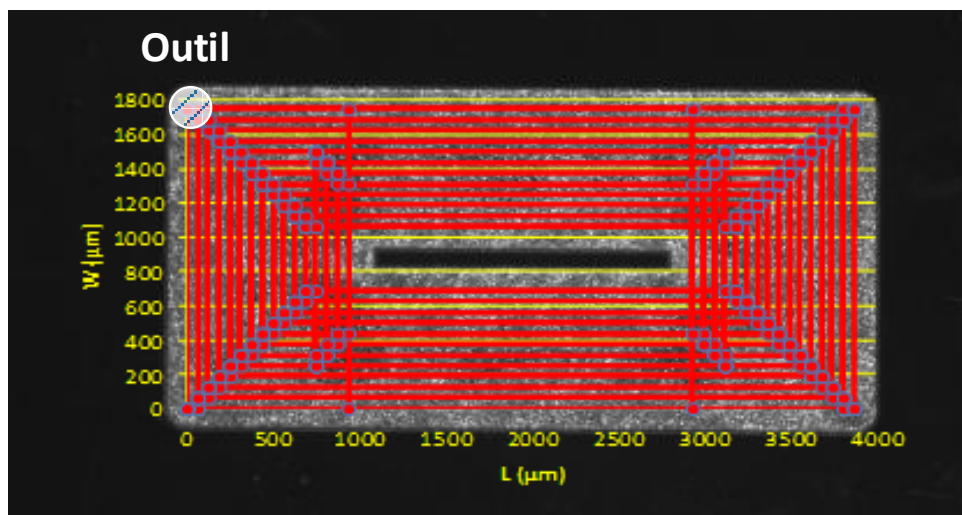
Usinage d'un insert avec $R=75\%$: parcours d'outil d'une couche en rouge superposé au résultat d'usinage (photographie).
